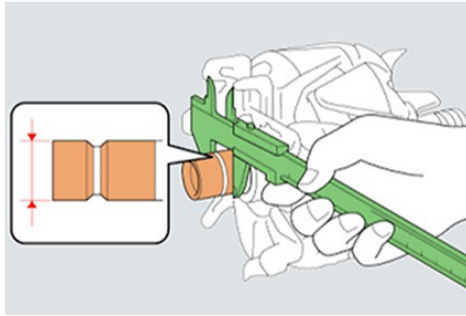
Перевірка контактних кілець з допомогою штангенциркуля
